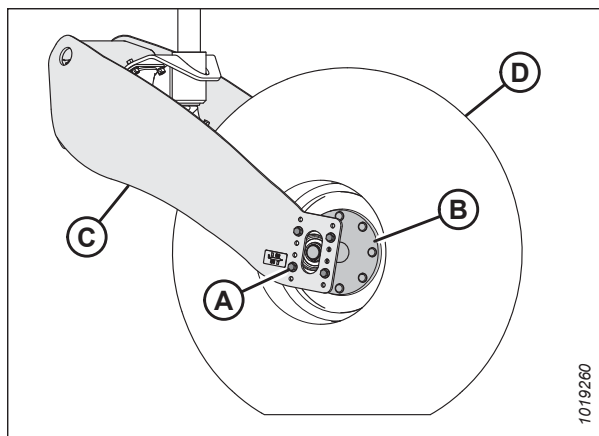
Самоустанавливающееся колесо в сборе
